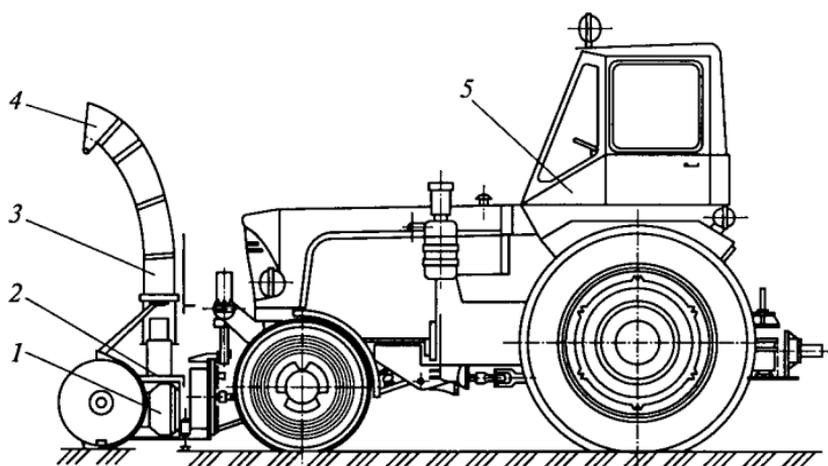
Фрезерно-роторное оборудование УСБ-25Р:
